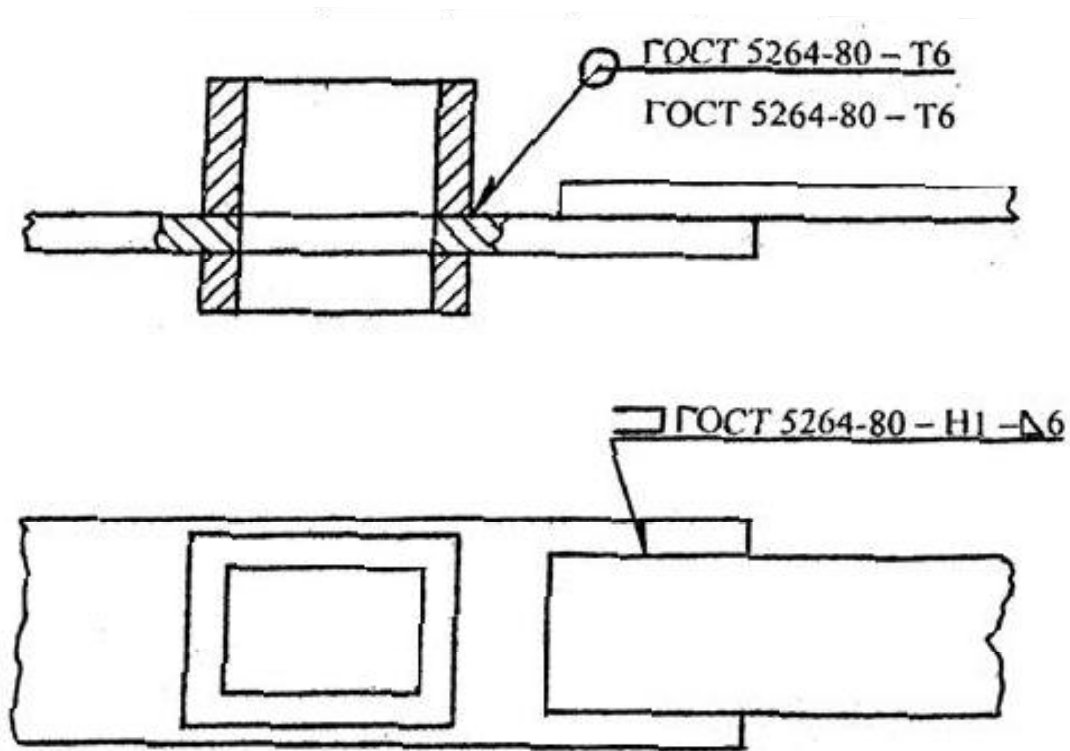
Структура условного обозначения сварного шва
